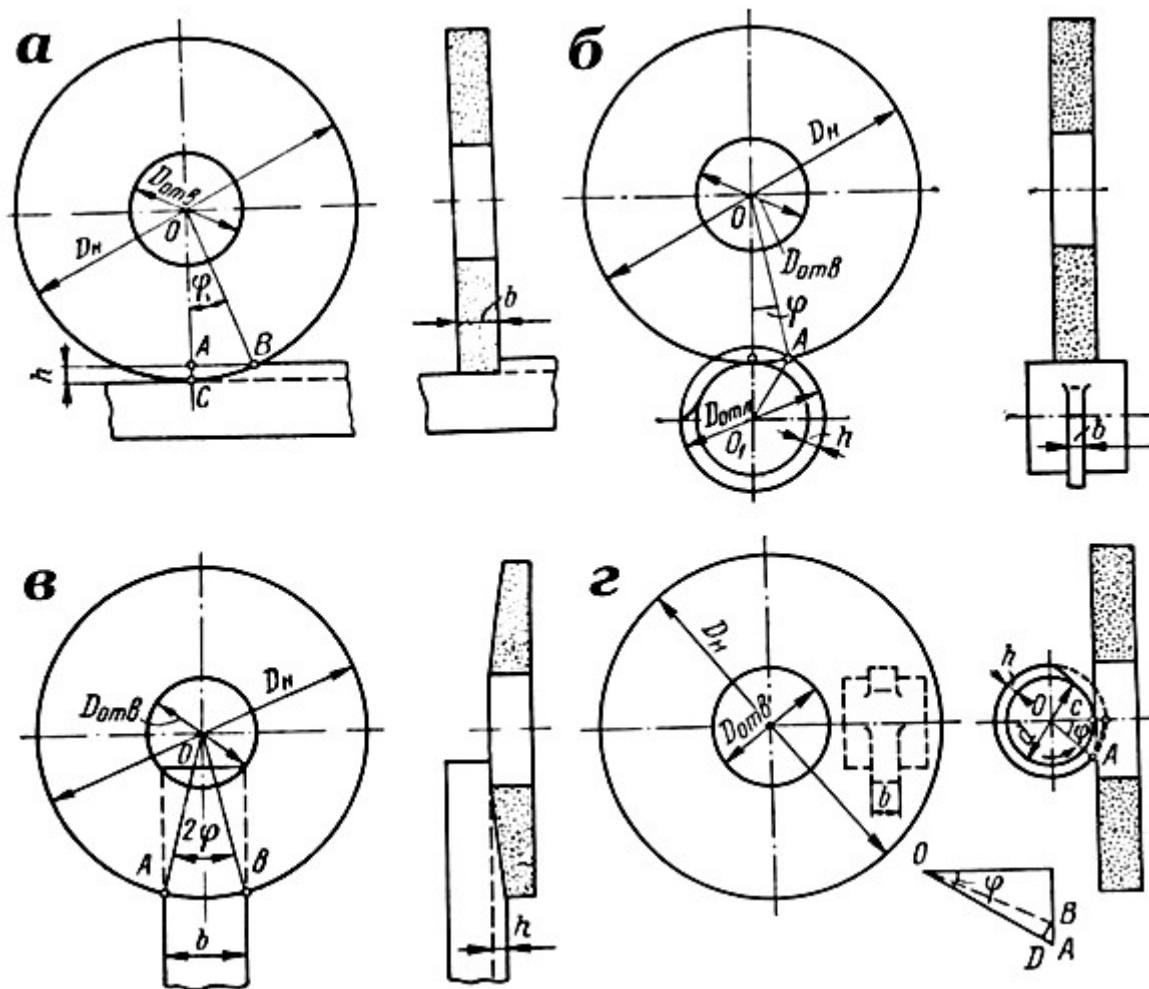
Схемы абразивной обработки: а – плоской поверхности периферией круга; б – цилиндрической поверхности периферией круга; в – плоской поверхности торцом круга; г – цилиндрической поверхности торцом круга
